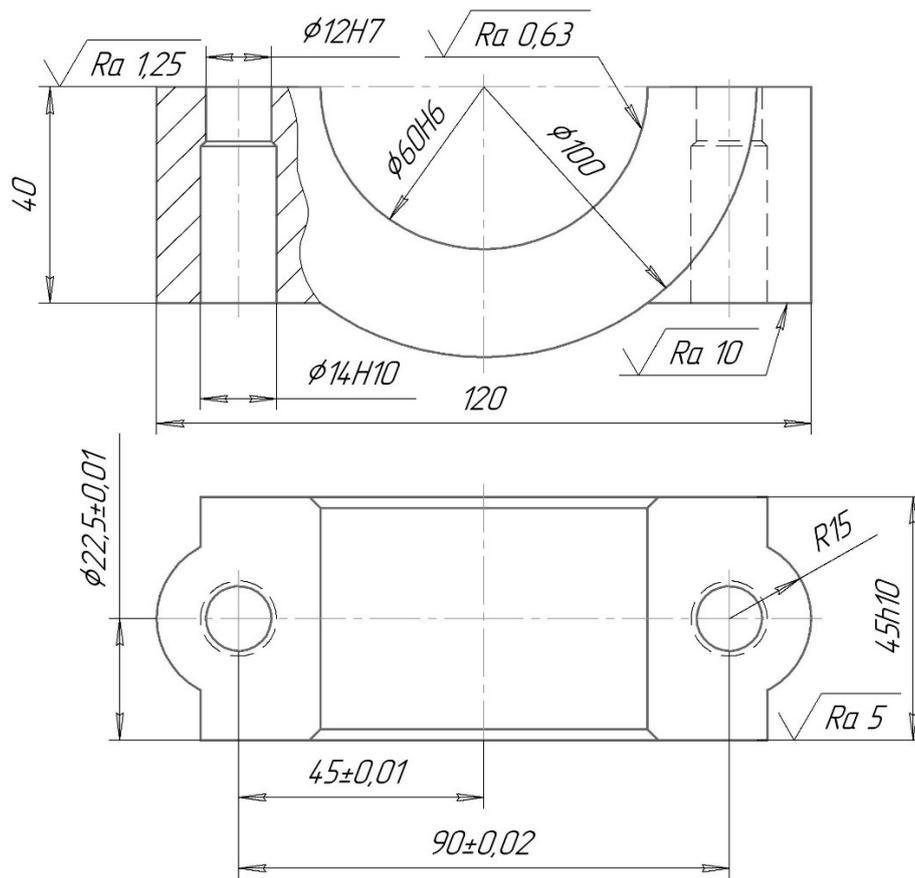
Эскиз детали – бугель коренной шейки коленвала
